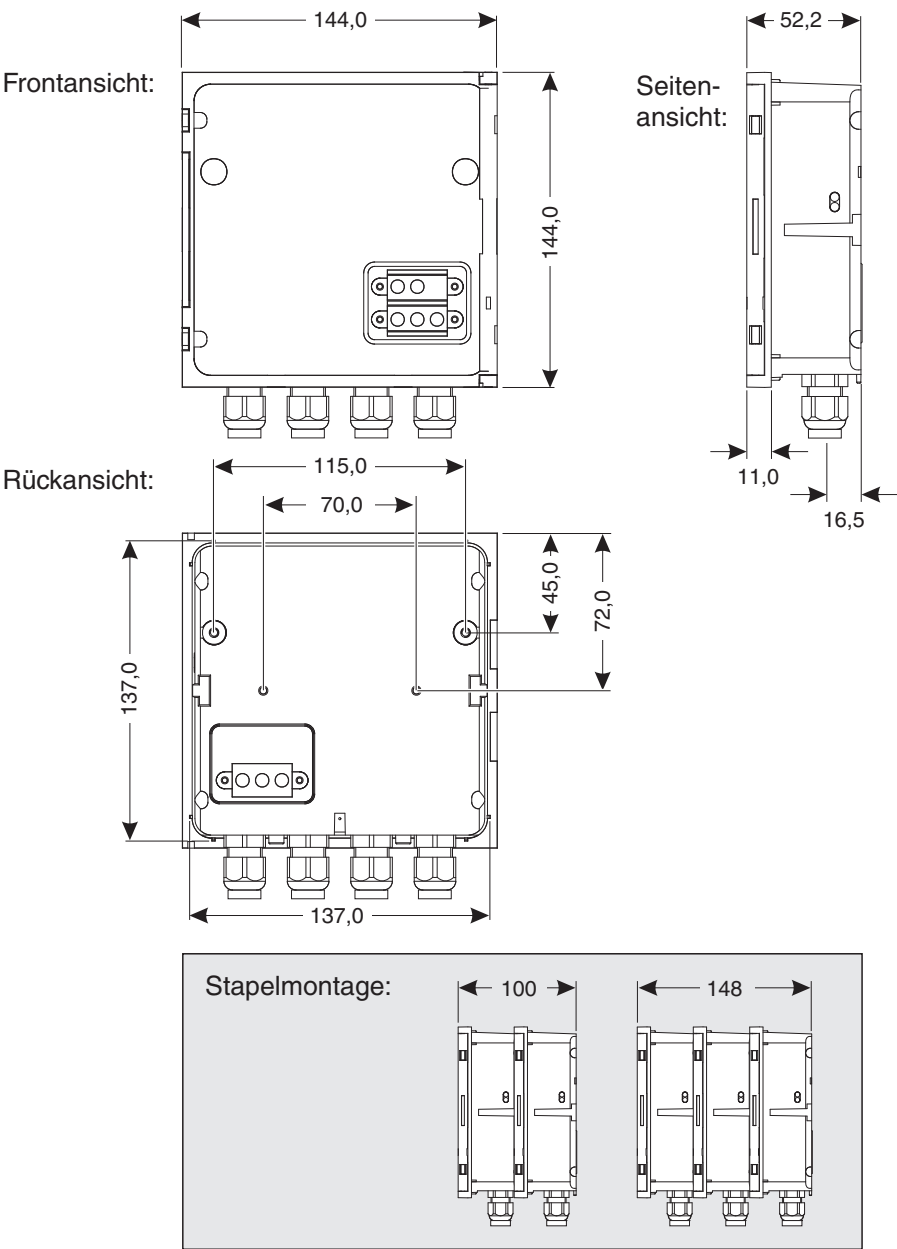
Maßzeichnung MIQ Modul (Maße in mm)
